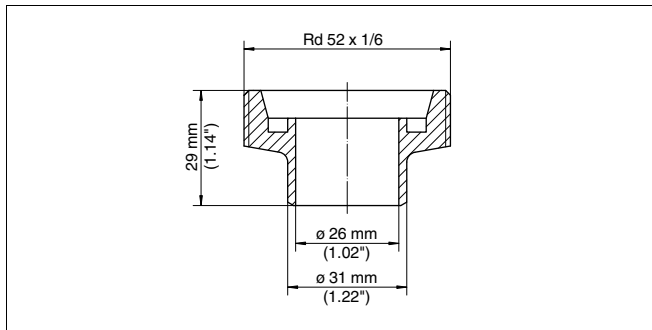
Размеры приварного штуцера - накидная гайка DN 25 по DIN 11851
